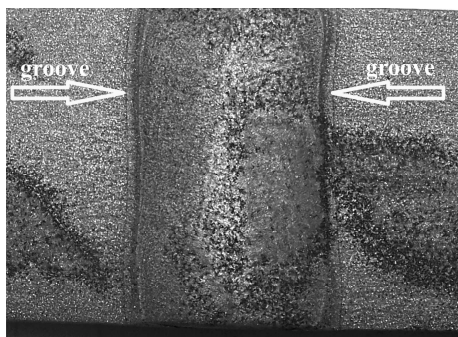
Зона шва стикового зварного з'єднання після корозійних випробувань.
